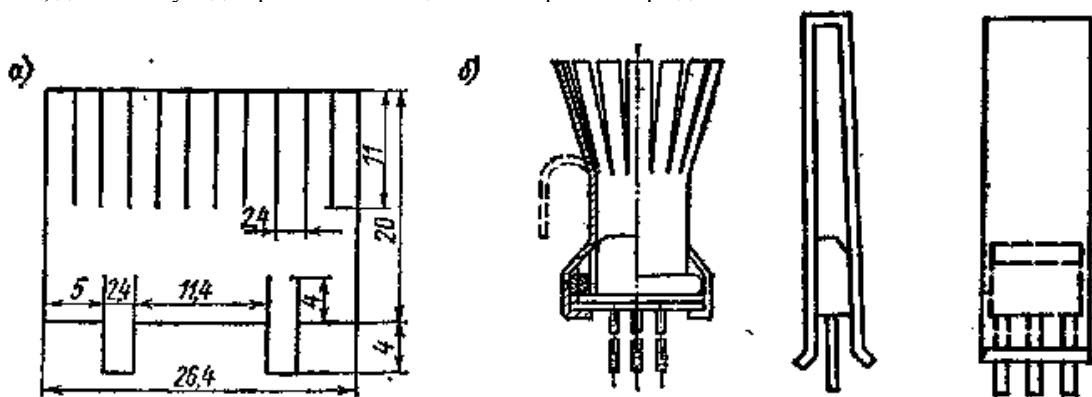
Радиатор для маломощного транзистора: а — развертка; б — общий вид
